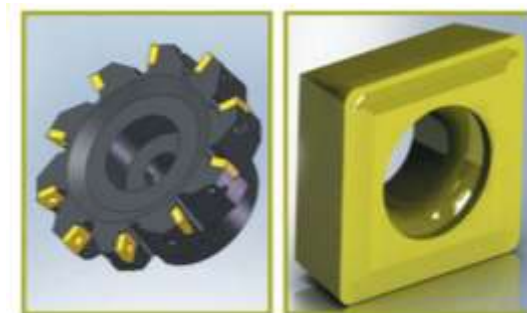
Торцева фреза та ріжуча пластина
